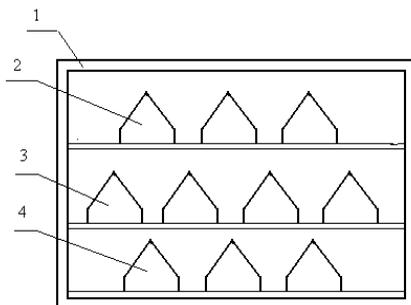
Секция шахты зерносушилки новой конструкции:
